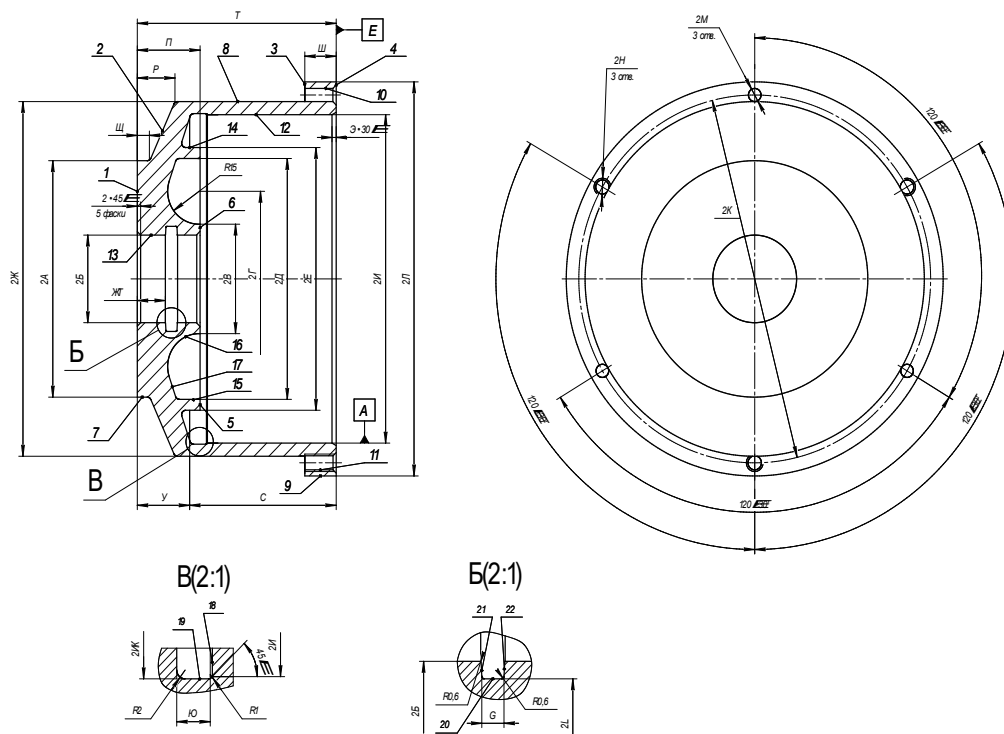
Креслення деталі корпусу гідроциліндра з позначенням її поверхонь
